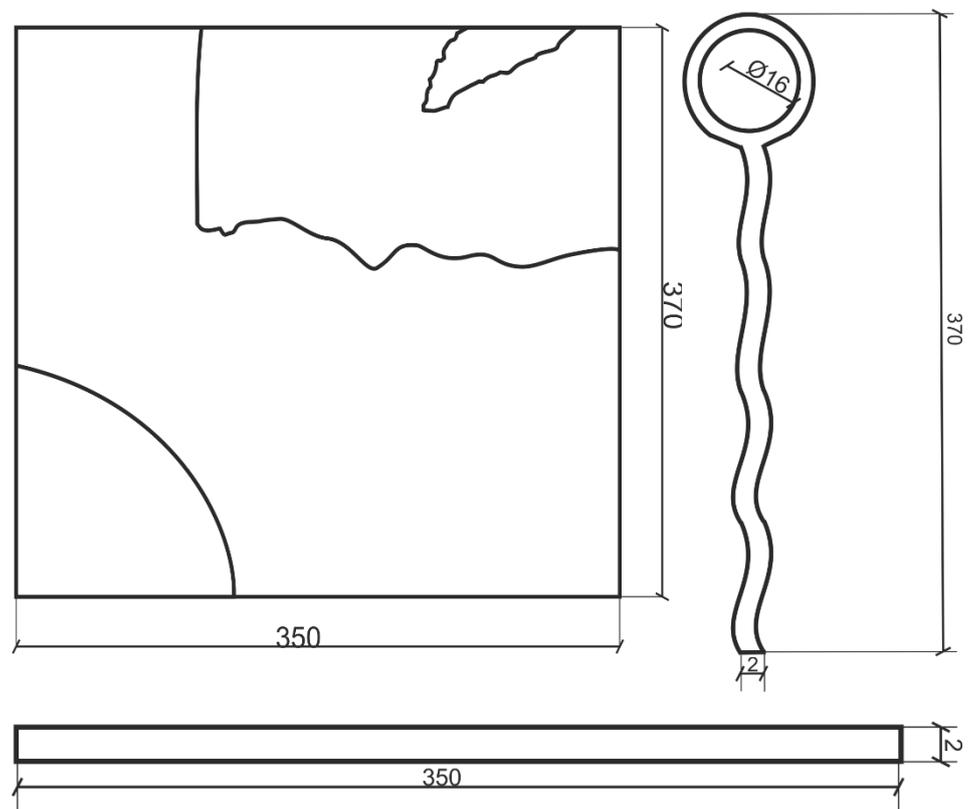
Mapa de medidas. Alzado, perfil y planta de la pieza 10.
